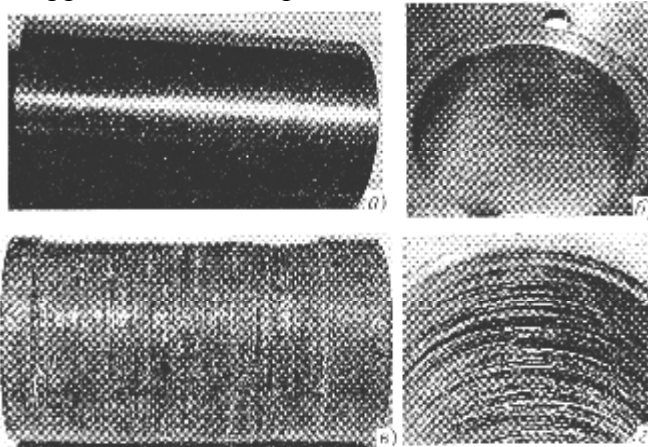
Фотографии втулок вала (а) и подшипника (б) до испытаний и наружной поверхности втулки вала (в) и внутренней поверхности втулки подшипника (z) после 950 ч работы
